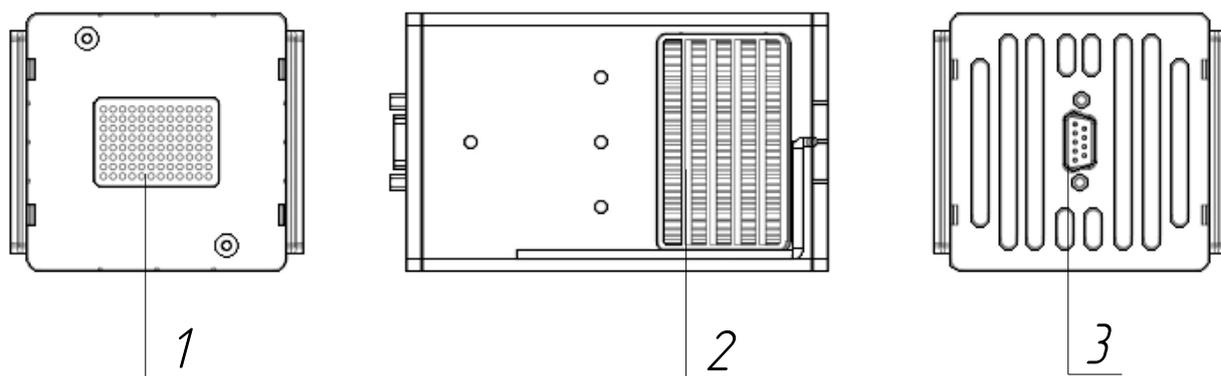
Внешний вид УФ-ламп 9LN3734 и 9LN2536. Условные обозначения:
